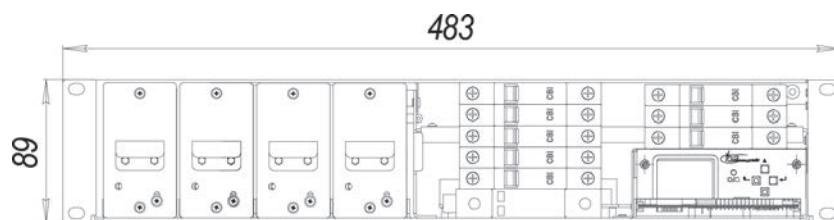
Габаритный чертеж УЭПС-3К-1кВт
